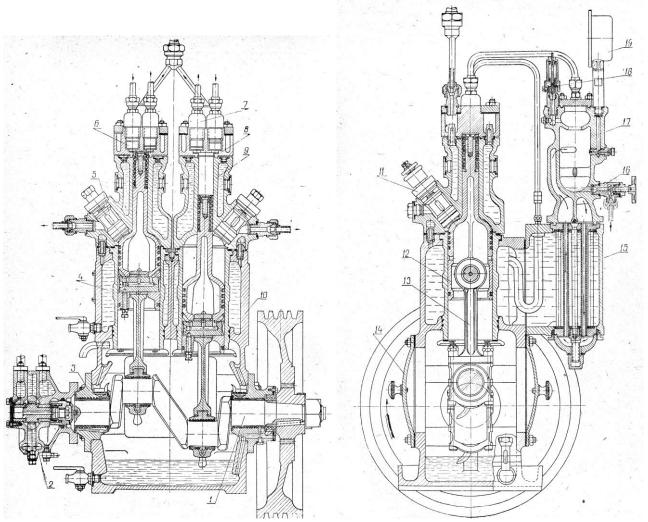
Продольный и поперечный разрезы компрессора 2 ОК-1
